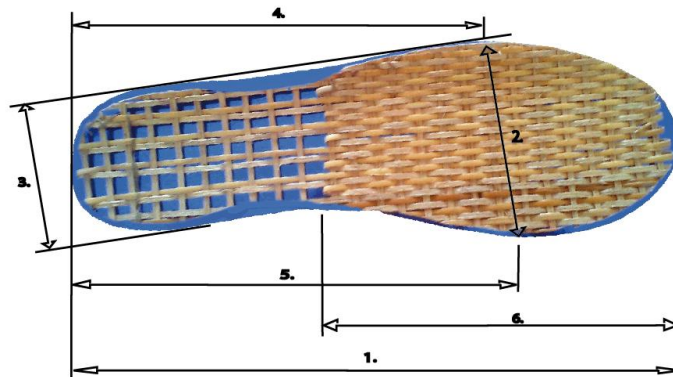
Planteamiento de tejido para la extracción de varias plantillas
